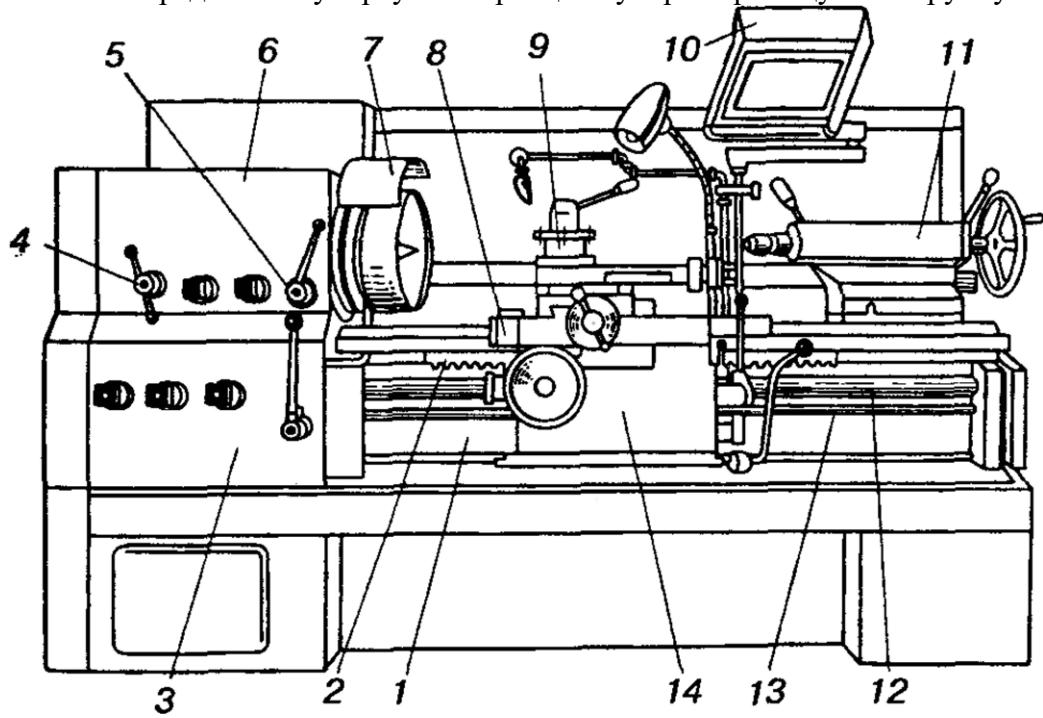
Загальний вигляд токарно-гвинторізного верстата 16К20
